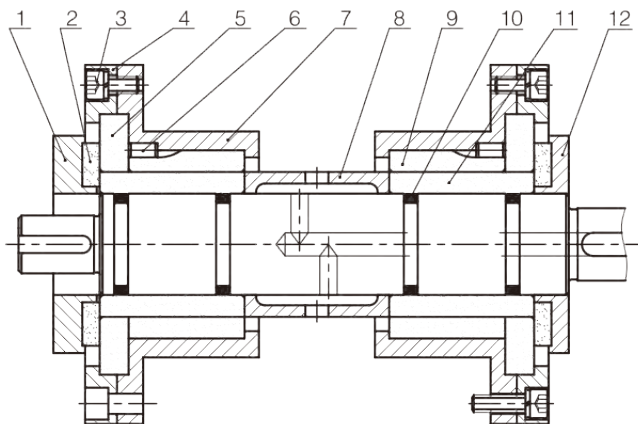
滑动轴承组件 fig.5: sliding bearing assembly
